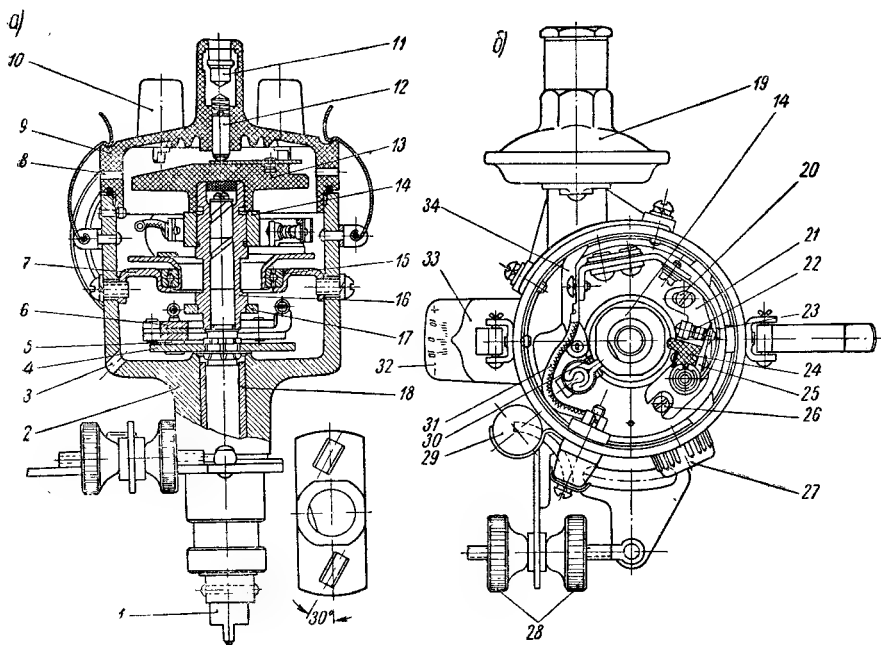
Прерыватель-распределитель Р-ЗБ: а — продольный разрез прерывателя-распределителя; б — вид на прерыватель-распределитель со стороны прерывателя:
